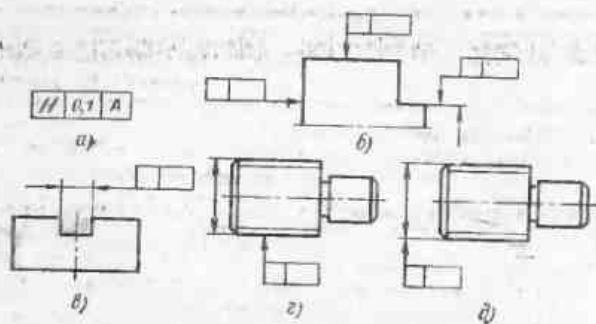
Схемы указания на чертежах допусков формы и расположения поверхностей
